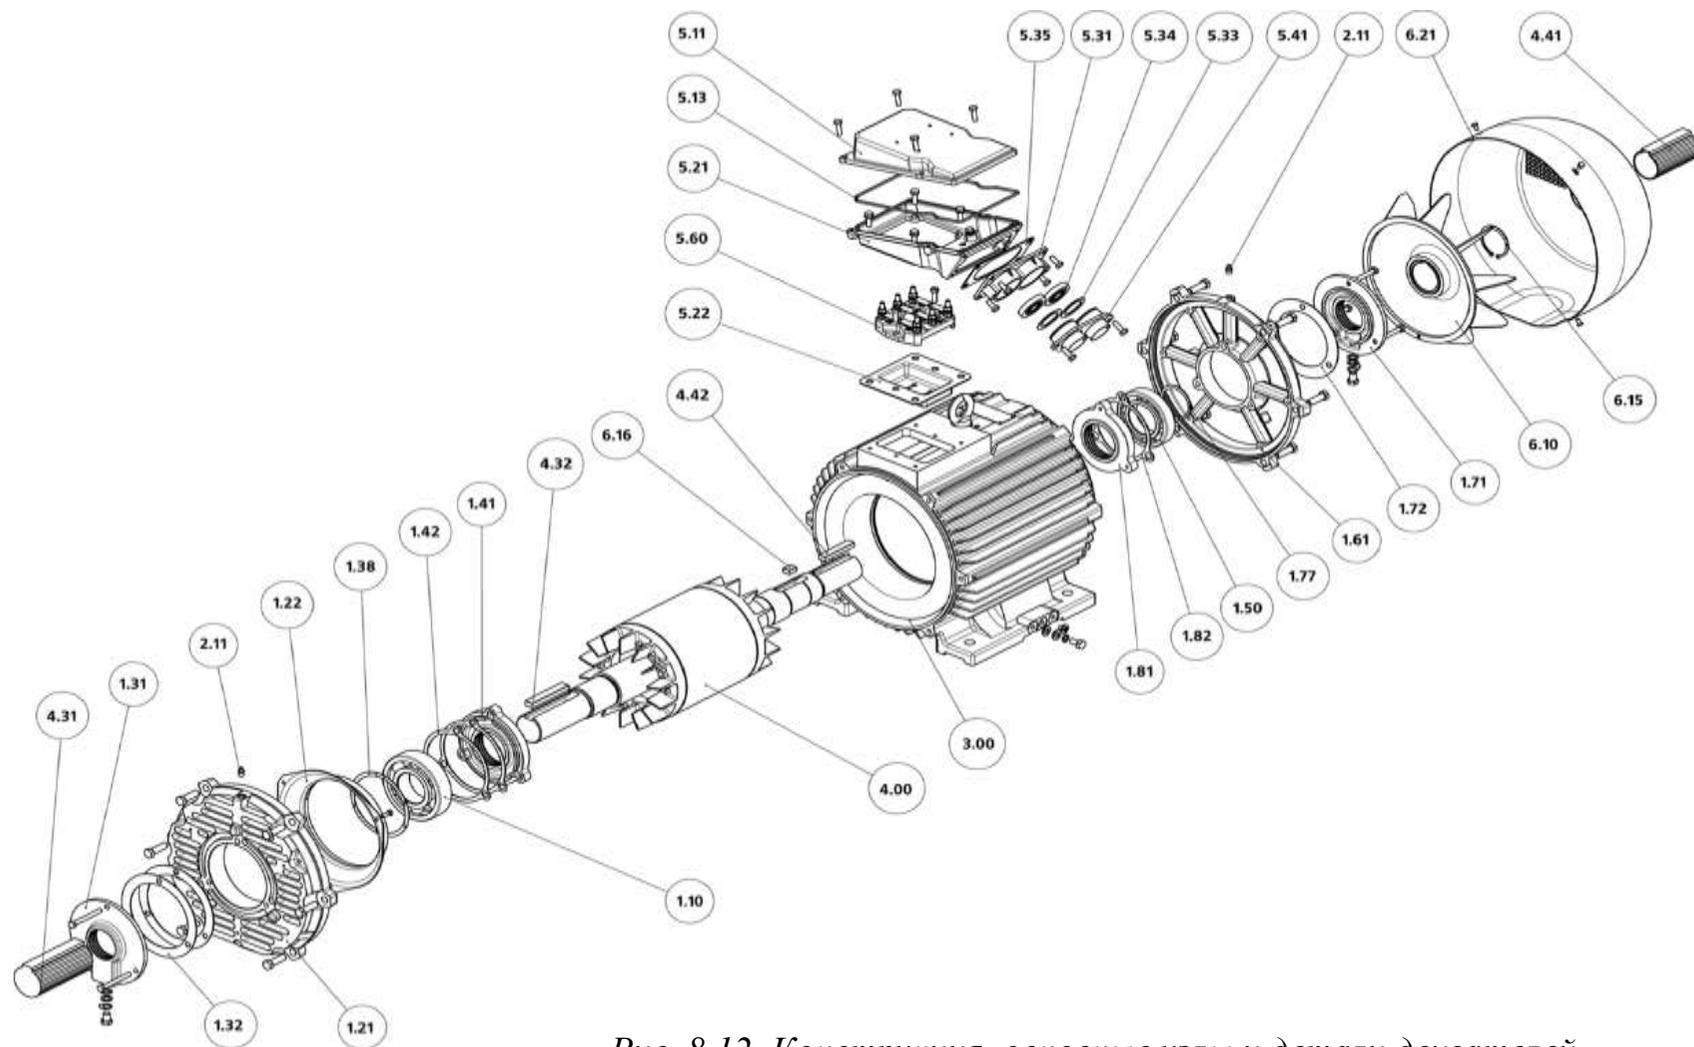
Конструкция, основные узлы и детали двигателей с высотой оси вращения 200 мм, степень защиты IP23
